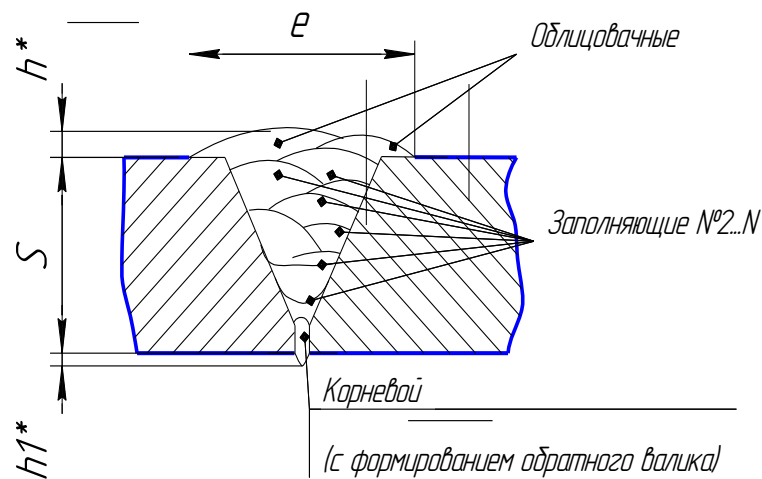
Размеры сварных швов  $h$ ,  $h_1$  согласно требованиям чертежа на деталь с кольцами
